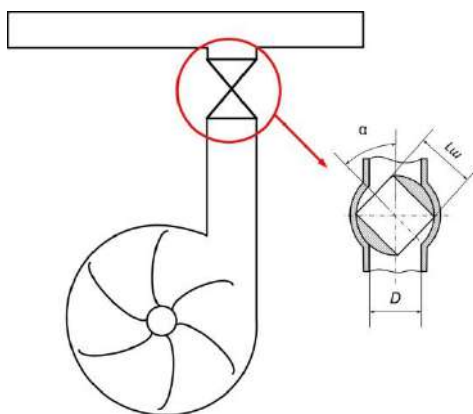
Схема дроссельной заслонки (шарового крана) в насосной установке.
